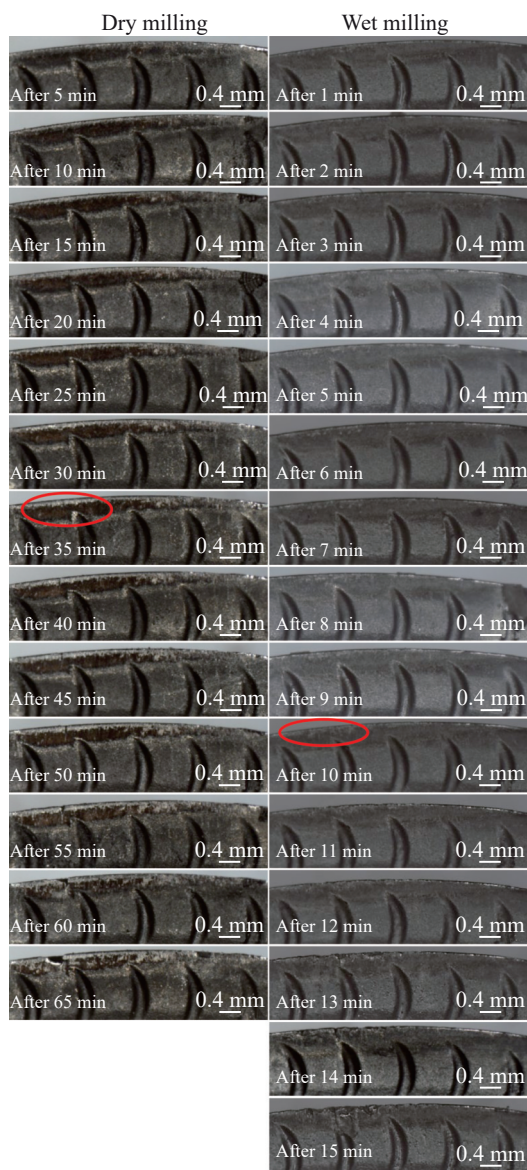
316L 不锈钢干、湿式铣削加工过程中 PT 刀具的失效演变
